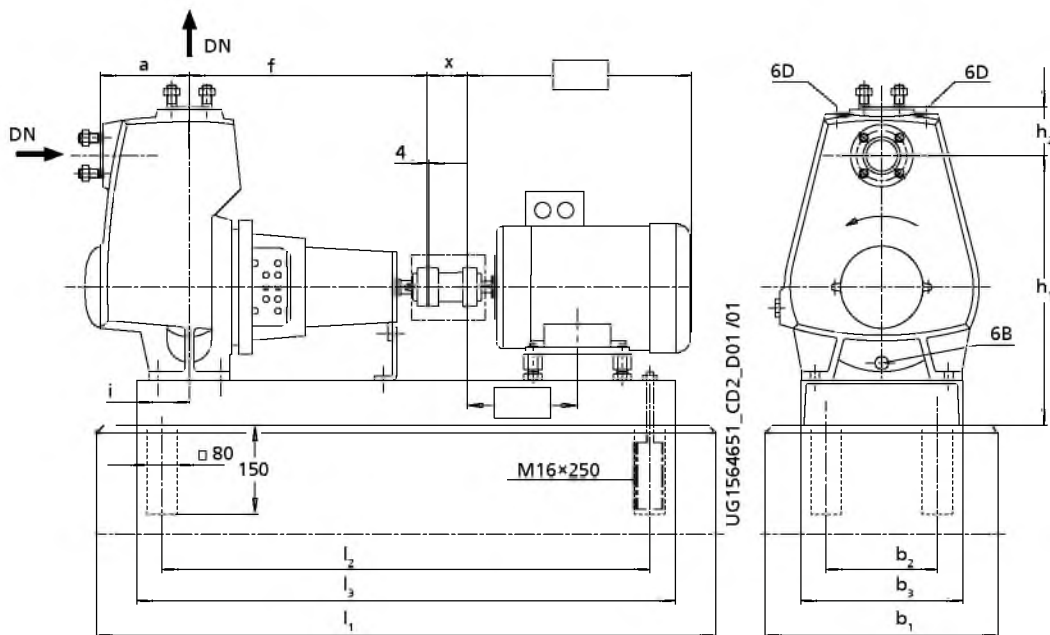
Габаритные размеры Типоразмер 040-040-140 до 125-125-260 (узел вала 25 / 35) – насосный агрегат с муфтой
